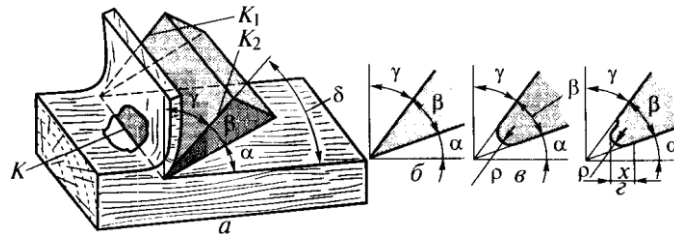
Елементи різця: а – поверхні і кути; б – вид дуже гострого різця; в, г – форми затуплених різців
